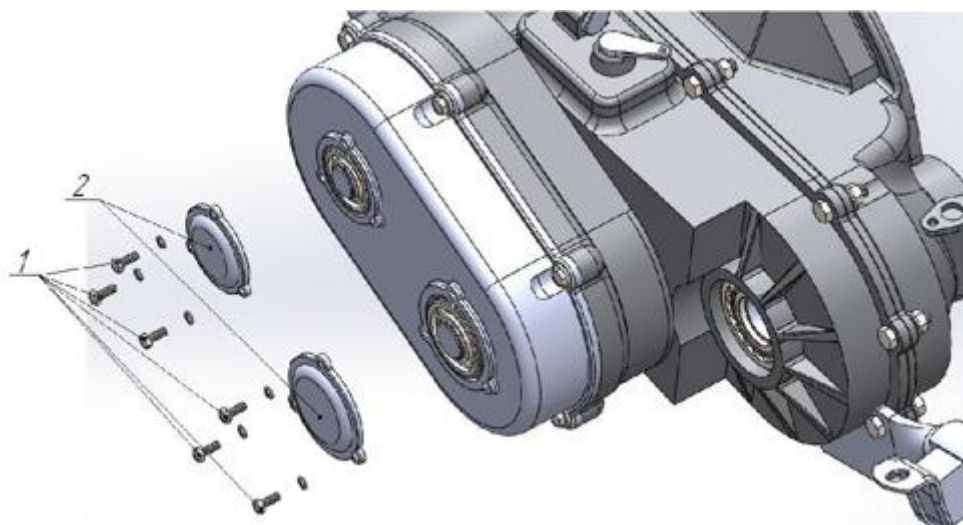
Клиноременная передача: 1 – крепежные винты; 2 – крышки подшипников
